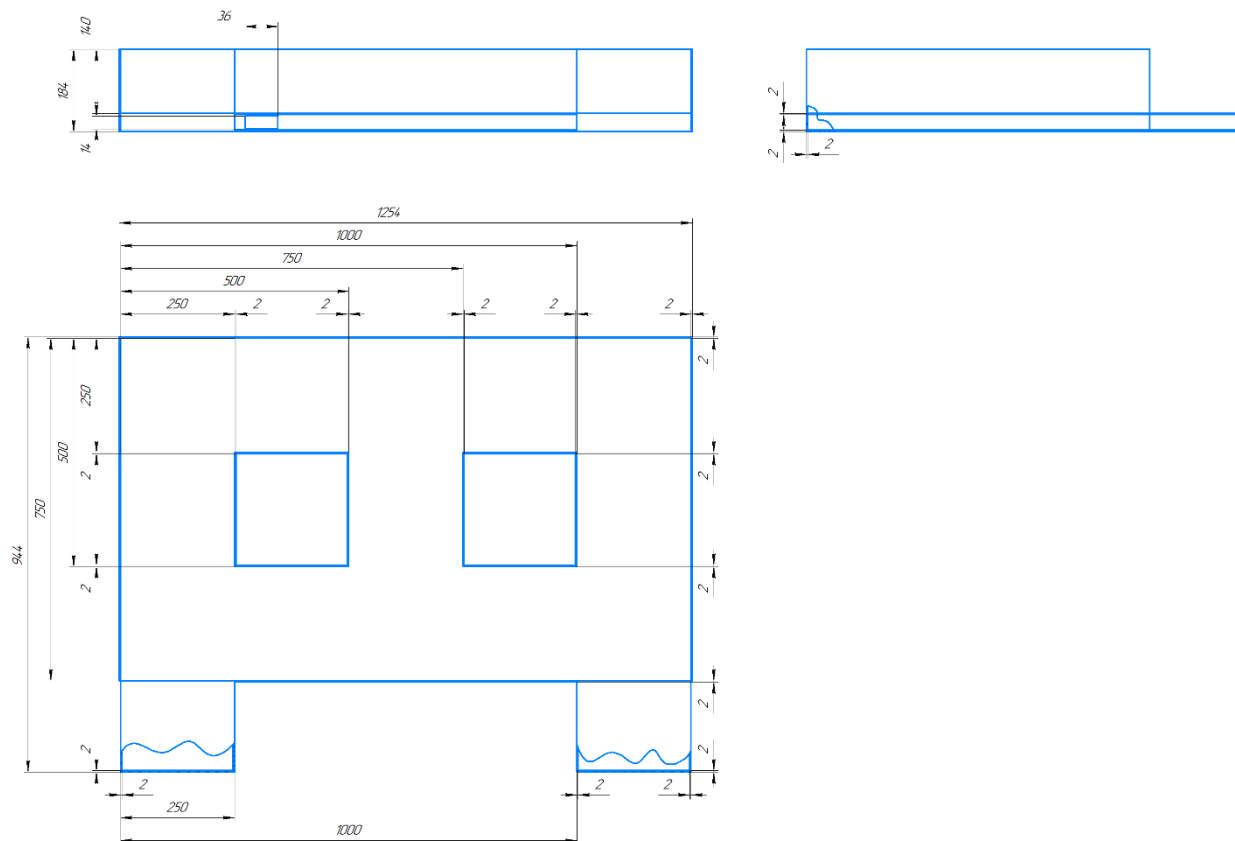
Габаритный чертёж макета мини-полигона
